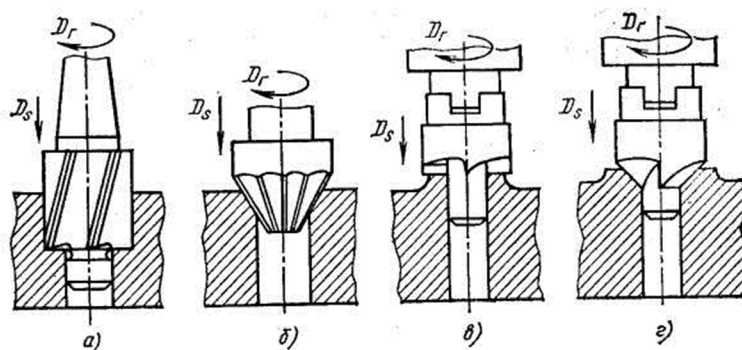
Схема обработки углублений и бобышек зенкерами и цековками
